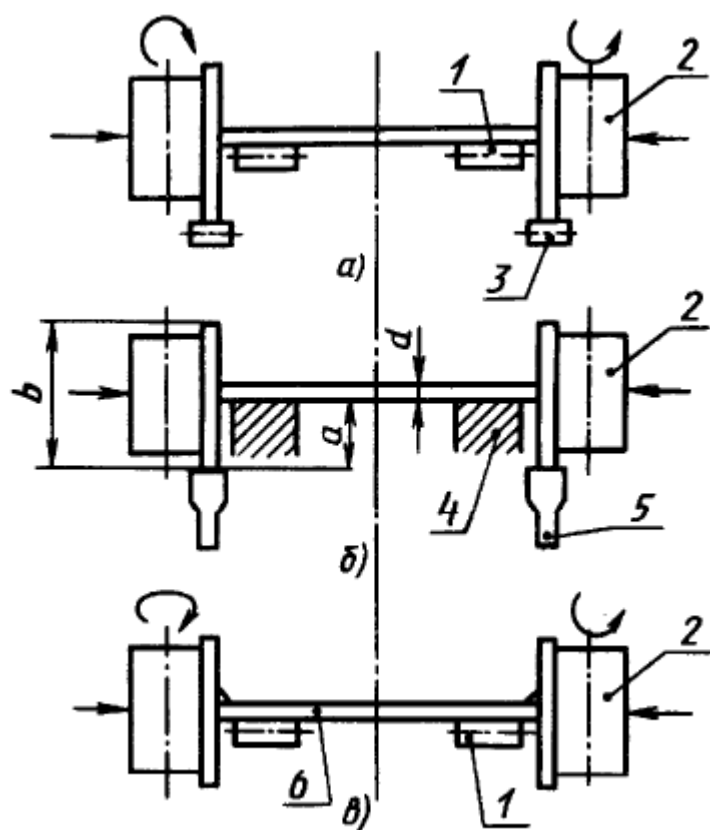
Схемы расположения опорных баз и прижимов сборочного стана
